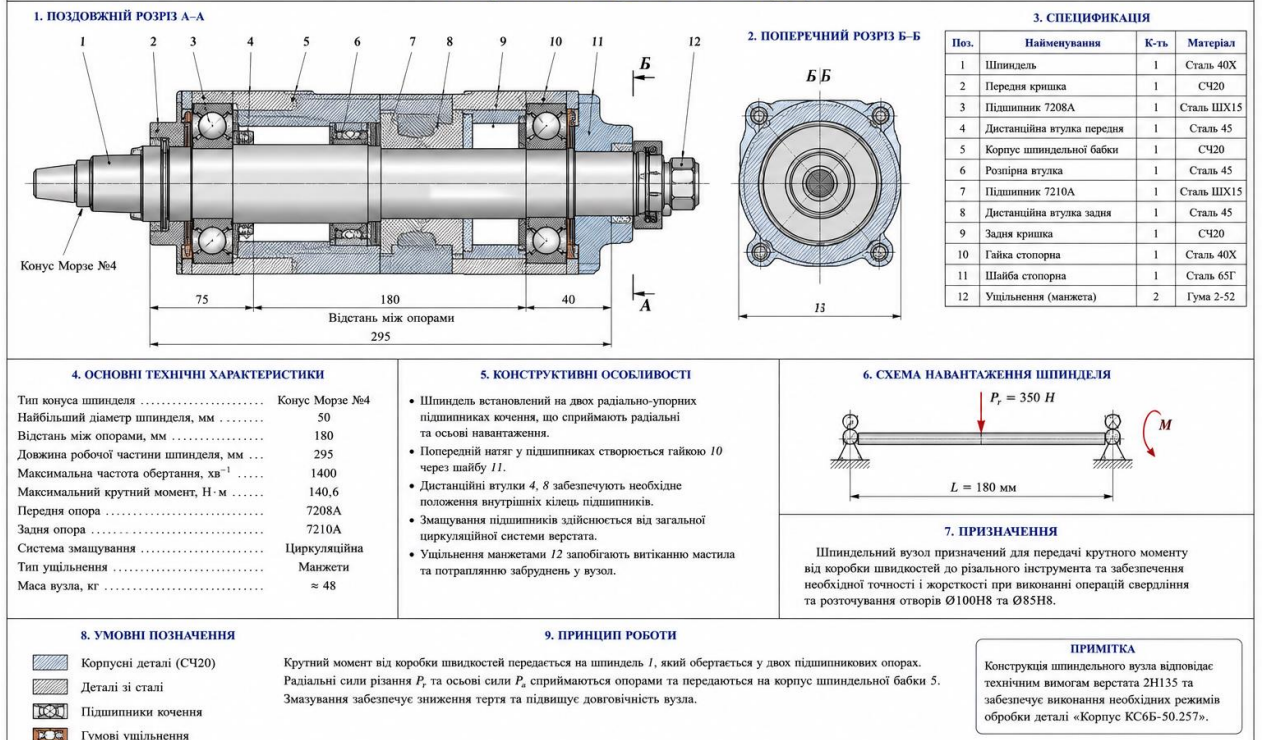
Шпиндельний вузол модернізованого приводу головного руху верстата 2Н135.
